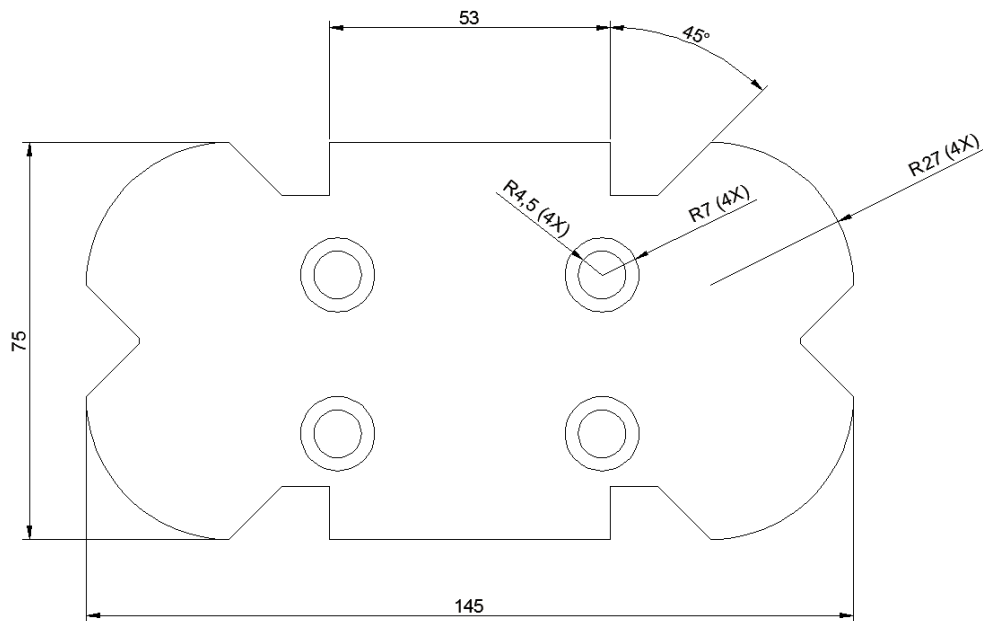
Desenho esquemático do corpo de prova (mm).
